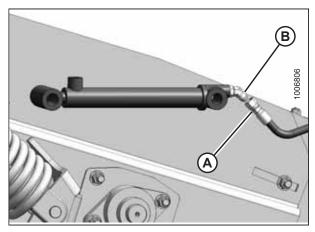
Cylindre asservi — Côté droit de la plateforme
